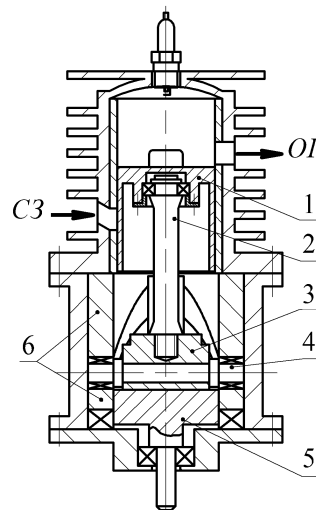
Схема бескривошипного двухтактного двигателя с вращающимся грузовым валом: 1 – поршень; 2 – шток; 3 – каретка механизма преобразования движения; 4 – ось каретки; 5 – выходной (грузовой) вал; 6 – вставки
